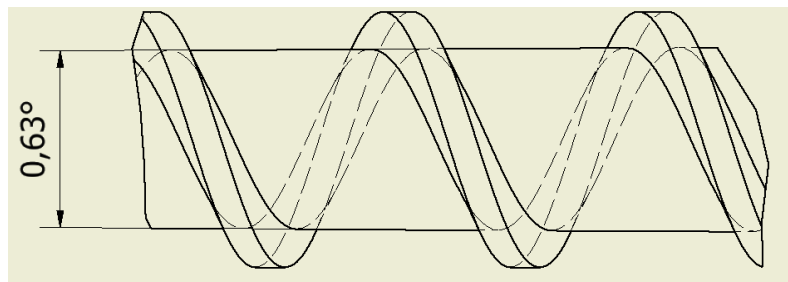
Filete para Husillo de máquina de extrusión y soplado
